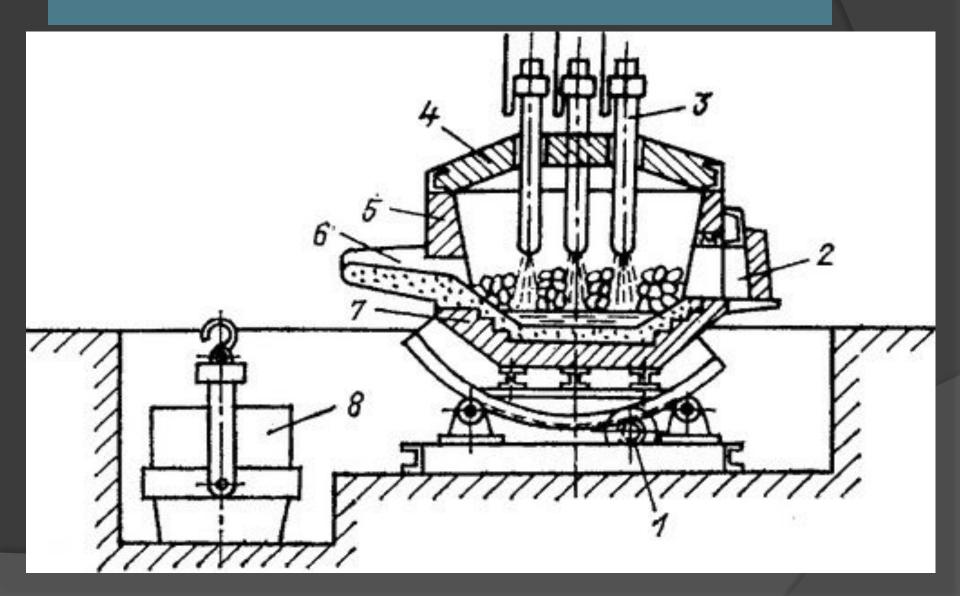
Схема трехфазной дуговой печи 1 — механизм поворота печи; 2 — загрузочное окно; 3 — электроды; 4 — свод; 5 — корпус; 5 — желоб для выпуска стали; 7 — под; 8 — разливочный ковш
